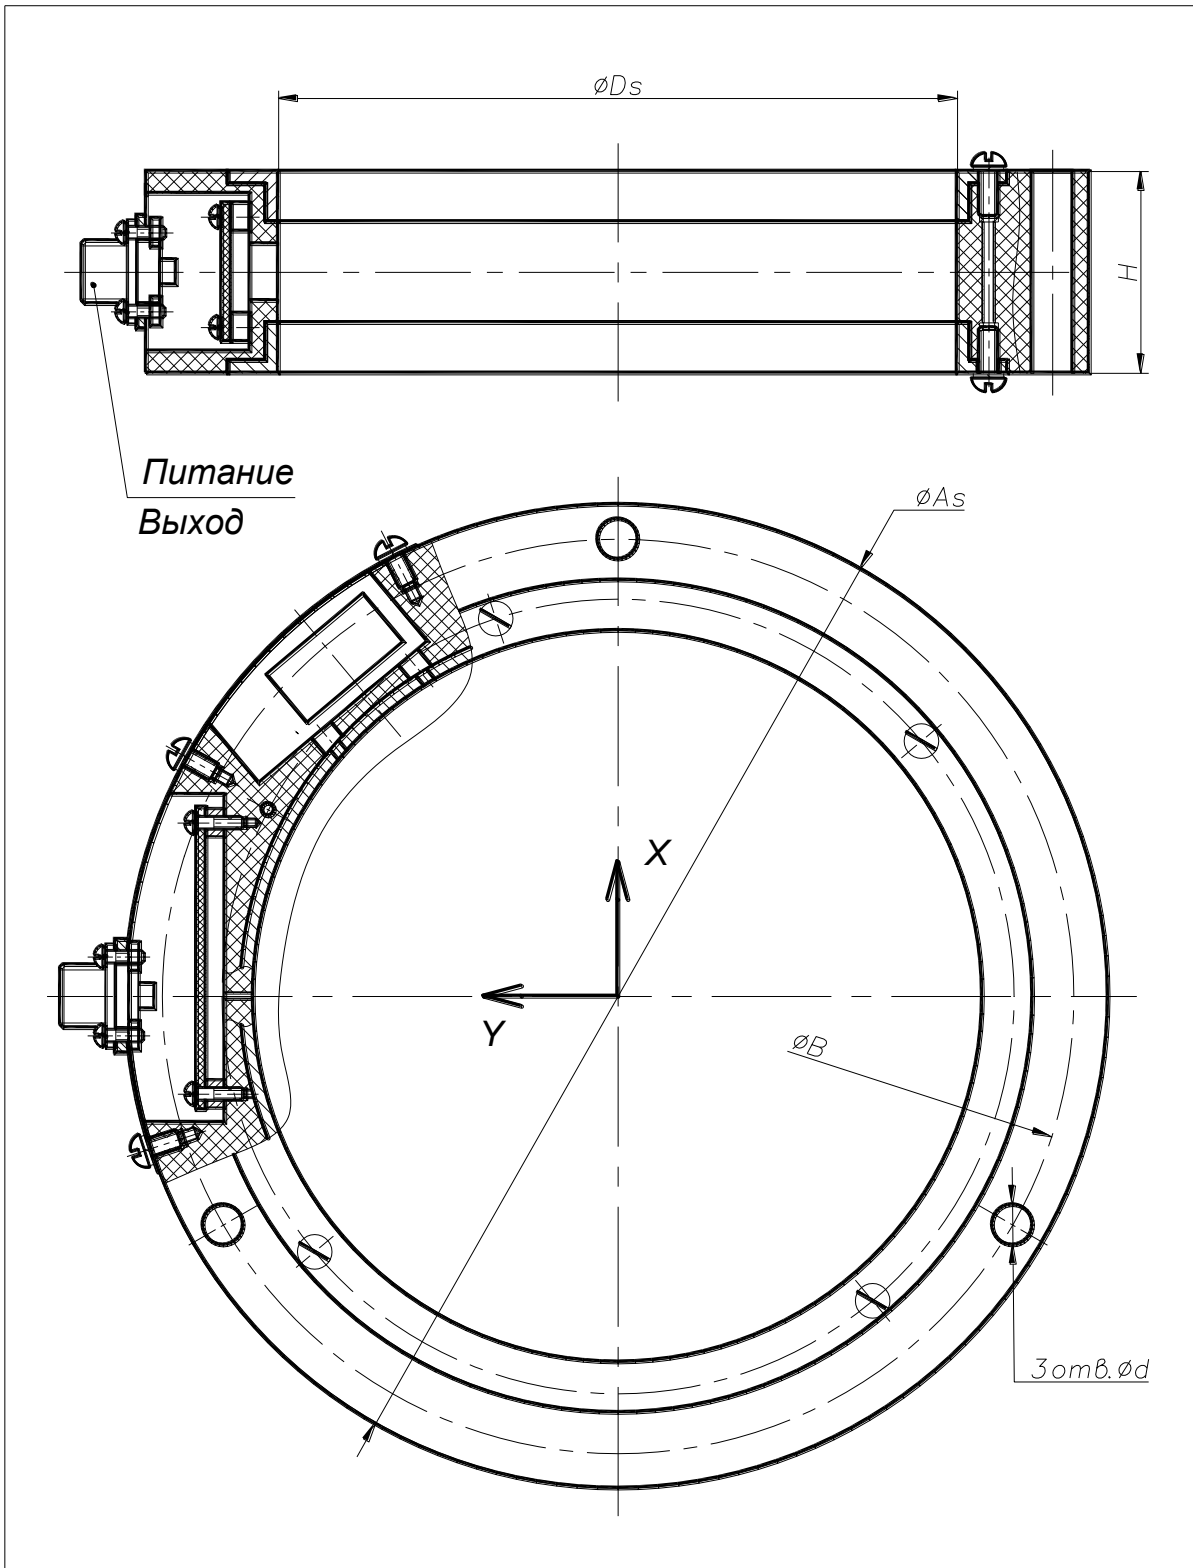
Датчик шестикомпонентный М46. Статор. Габаритные и установочные размеры, мм
